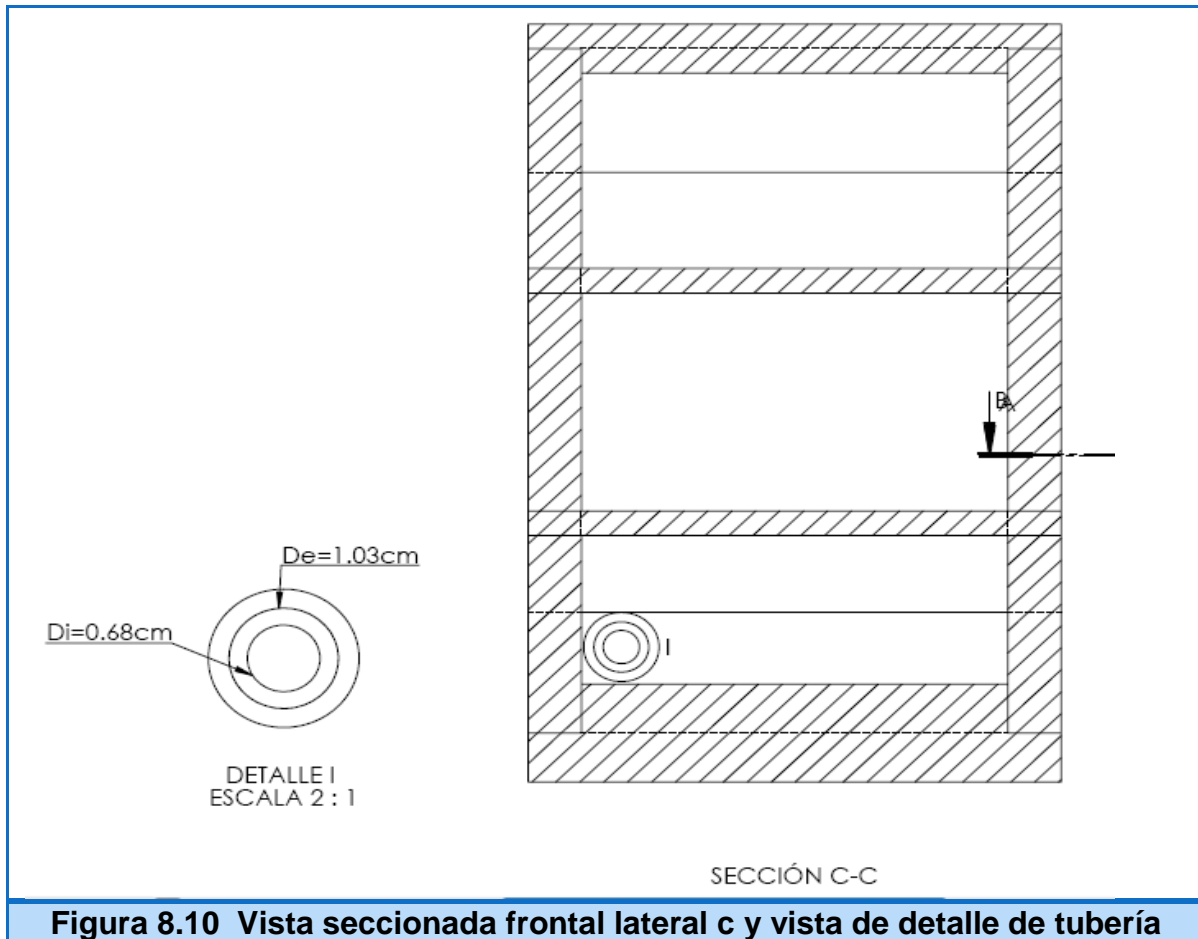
Vista seccionada frontal lateral c y vista de detalle de tubería
